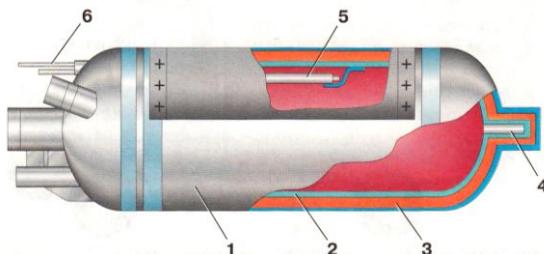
Газовый сосуд: 1 - кожух; 2 - внутренний сосуд; 3 - вакуумная рубашка; 4 - опорная втулка; 5 - ловушка; 6 - вакуумный вентиль
